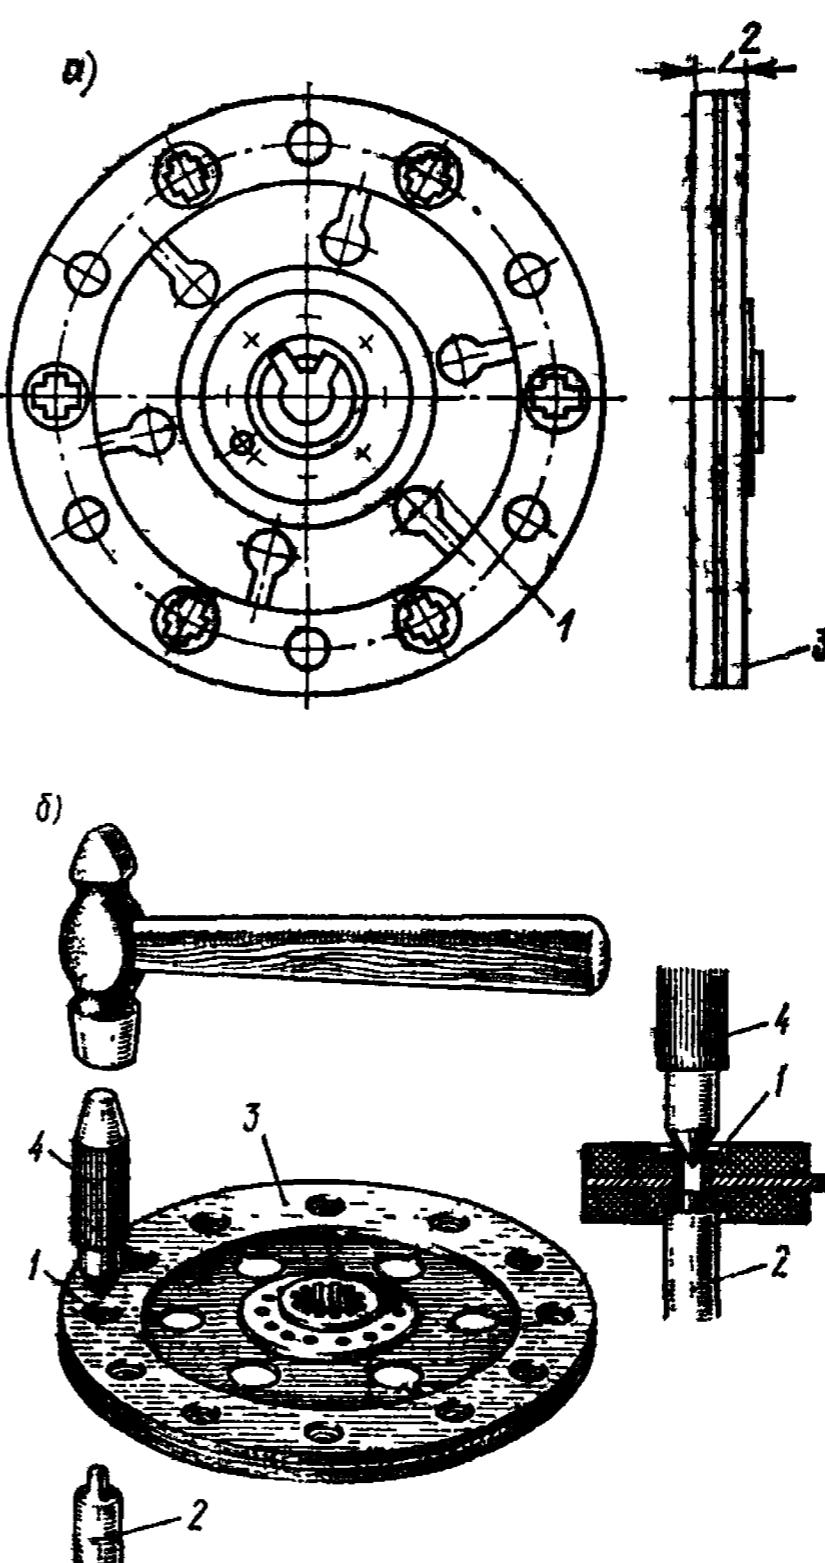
Диск сцепления ведомый: а — дефекты диска; б — установка накладок с помощью оправки:
